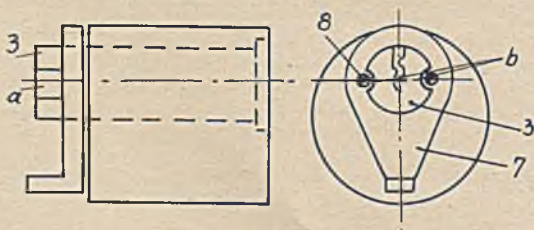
Schließnasenbefestigung durch zwei Schrauben, Zylinder angesent
